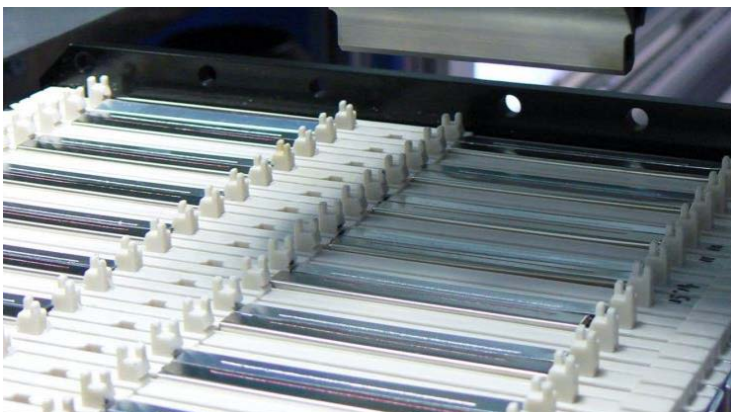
Verschweißen von Batteriezellen mit einer Laserprozessanlage
